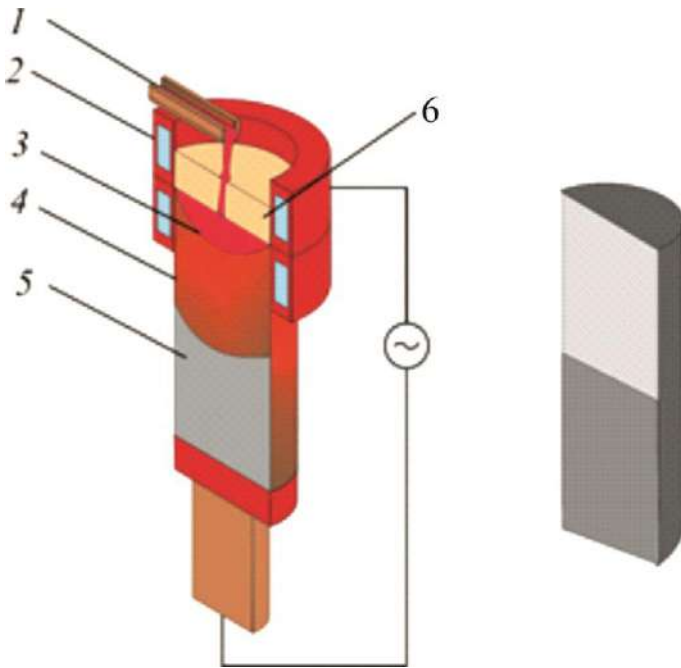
Схема виготовлення методом ЕШП РМ композитного злитку: 1 –пристрій для подавання рідкого металу; 2 – струмопідвідний кристалізатор; 3 – металева ванна; 4 – метал, що наплавляється, хімічного складу А (38ХНЗМФА); 5 – вихідна заготовка хімічного складу Б (12Х13); 6 – шлакова ванна
